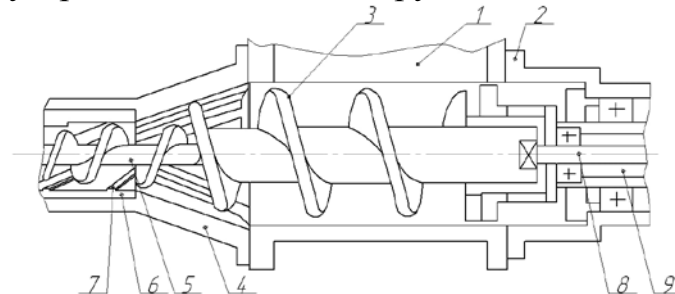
Пристрій для подрібнення м'яса : 1 - завантажувальний бункер; 2 - корпус; 3 - спіраль; 4 - хвостовик; 5 - шнек; 6 - робочий циліндр; 7 - ребра; 8 - вал; 9 - порожнистий вал
